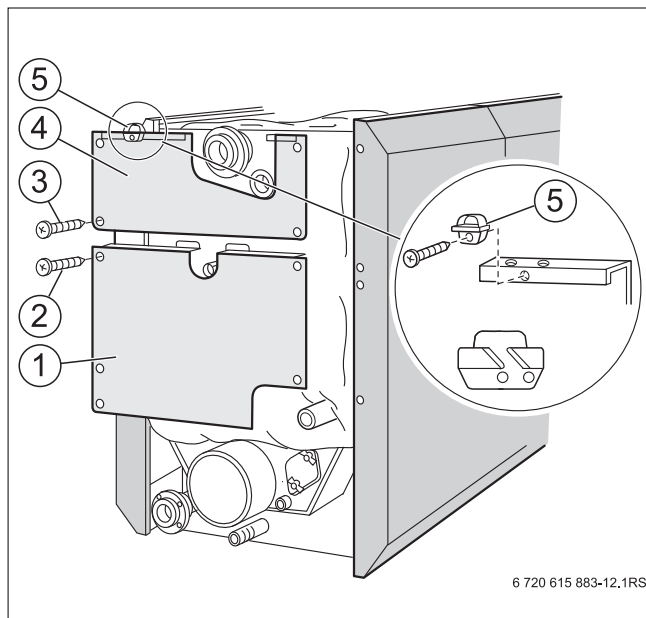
Zavěšení bočních stěn a připevnění kabelu hořáku
